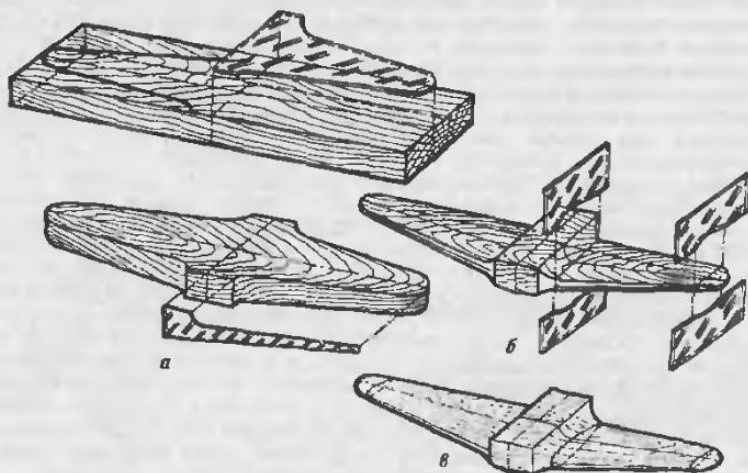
Последовательность изготовления крыла самолета-истребителя: а - разметка заготовки по шаблону "вид сверху" и "вид спереди"; б - профилировка крыла по шаблонам поперечных сечений; в - готовое крыло
